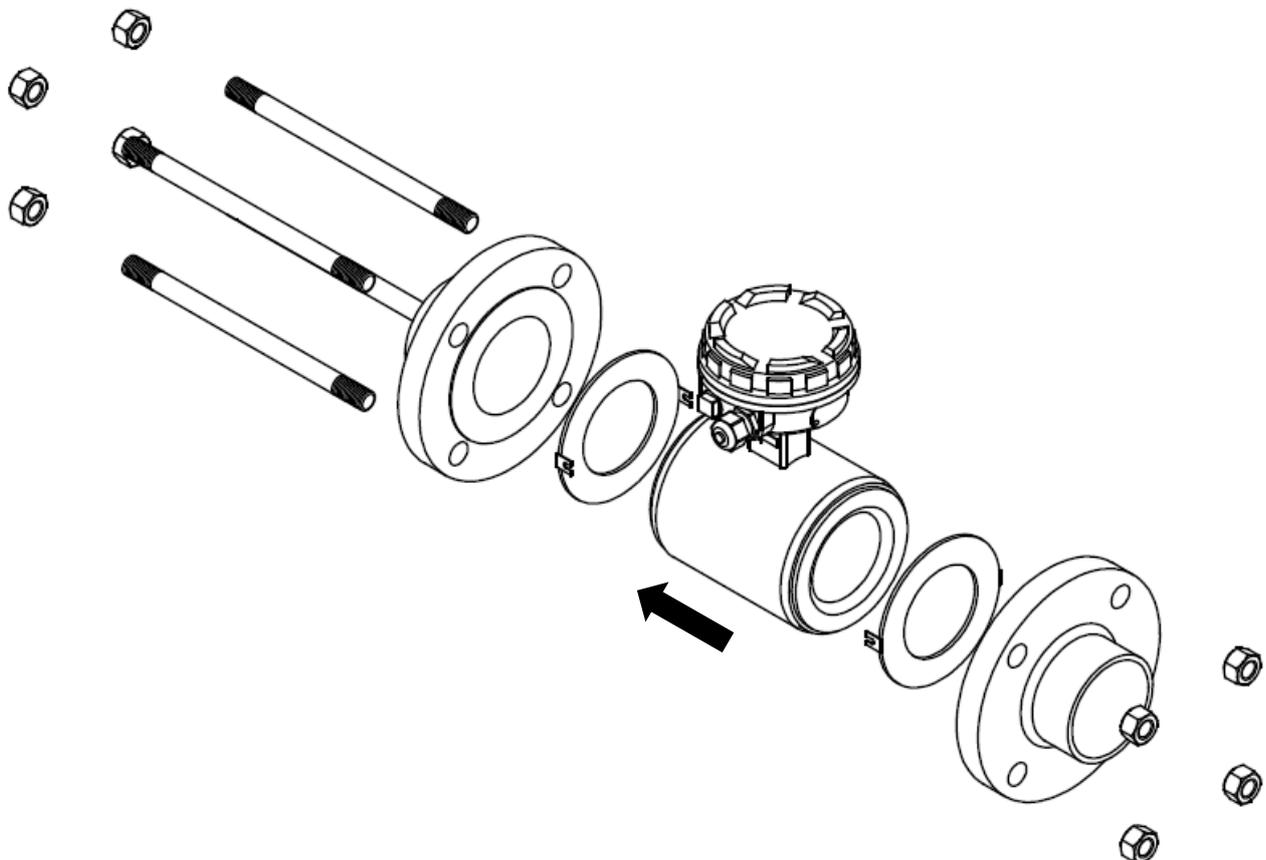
Montagem Medidor Waffer (DN 2" à 8") em vista explodida
